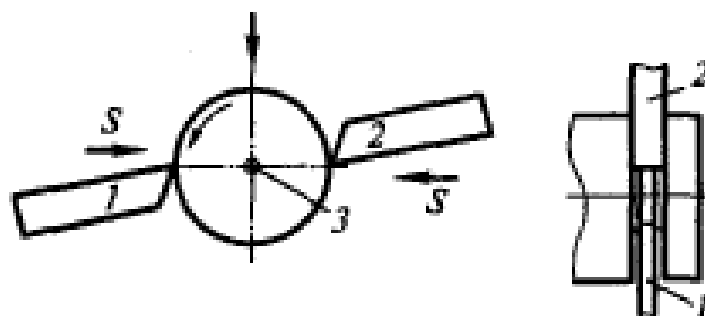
Схема відрізки на токарно-відрізному верстаті в двох проєкціях: 1 і 2 – різці; 3 – заготовка
